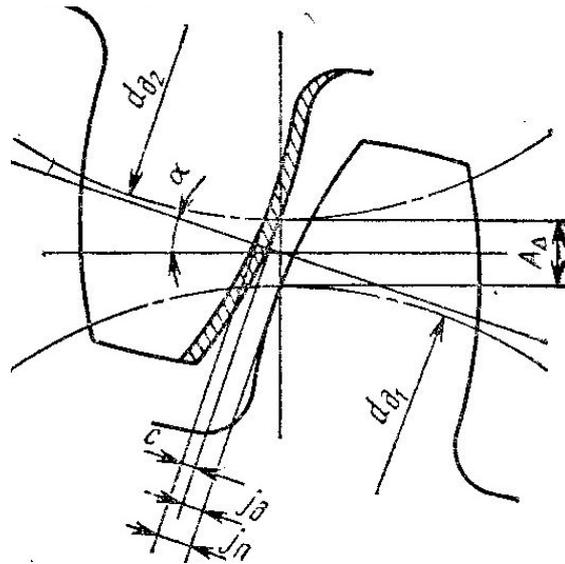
Составные части допуска на боковой зазор в зубчатом зацеплении:
